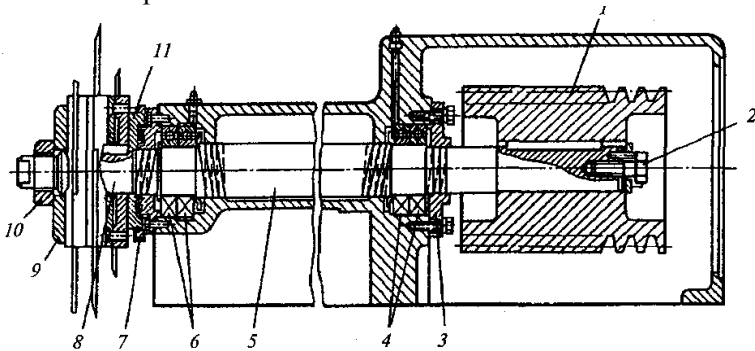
Ножовий вал куттера Л5-ФКМ: 1 – шків; 2 – болт; 3 – кришка; 4,6 – підшипники; 5 – вал; 7 – зовнішній лабіринт; 8 – ножова голівка; 9 – кільце; 10 – гайка; 11 – внутрішній лабіринт
